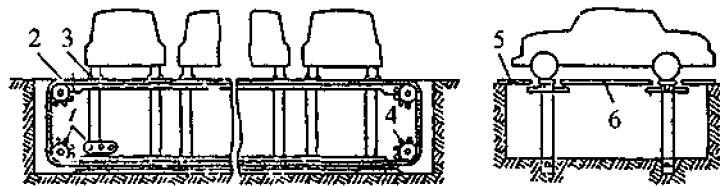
Схема двухветвевое цепного конвейера с поперечным расположением автомобилей:
